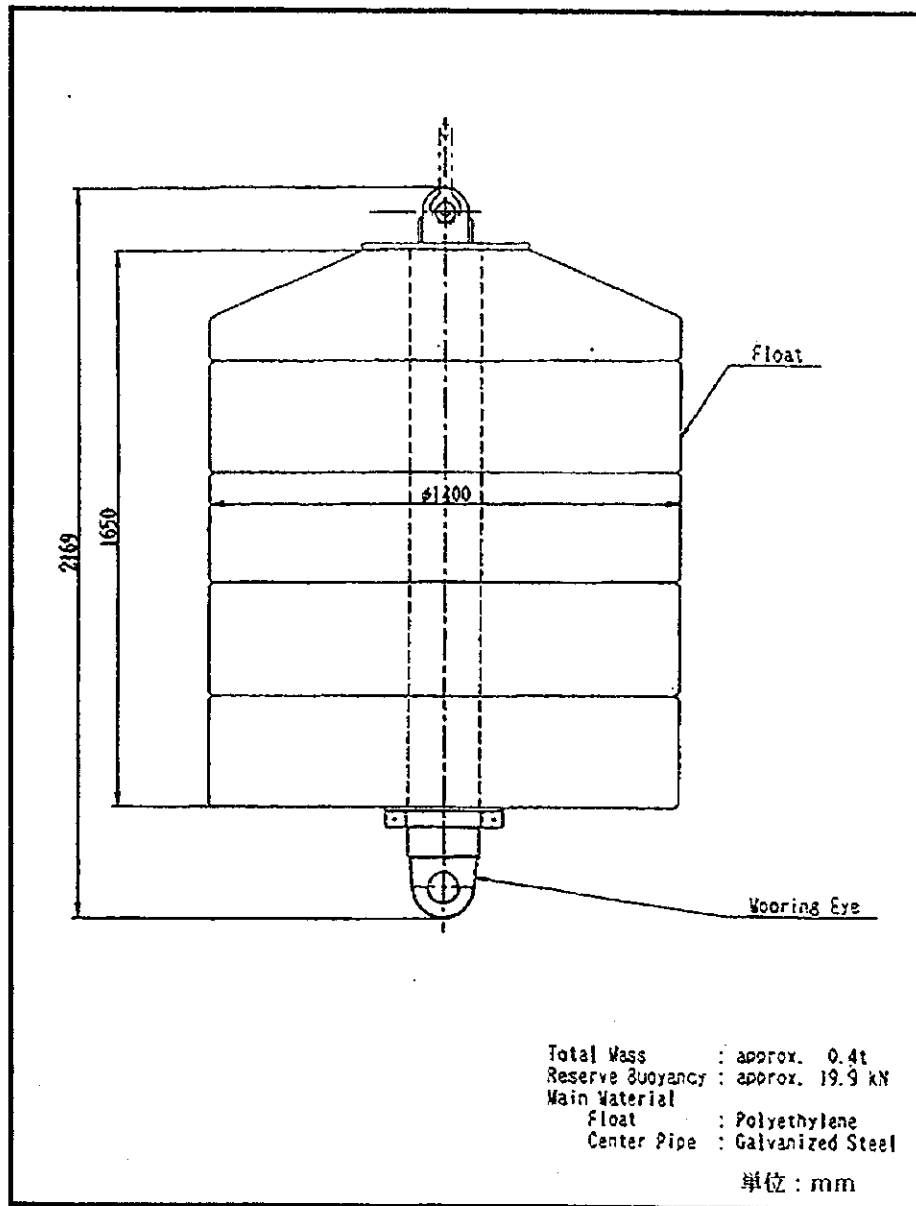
漁船用係留ブイの基本形状図(参考図)
